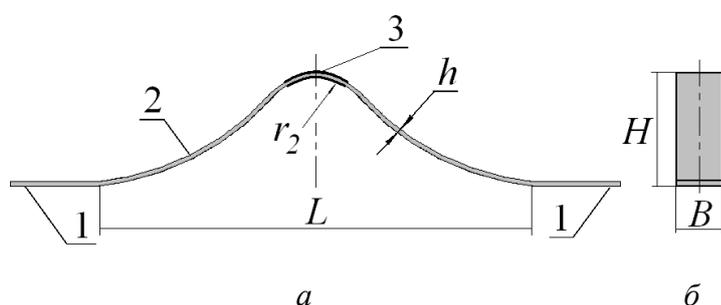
Общий вид арочного упругого элемента с вогнутым сводом: а – вид спереди, б – вид сбоку
